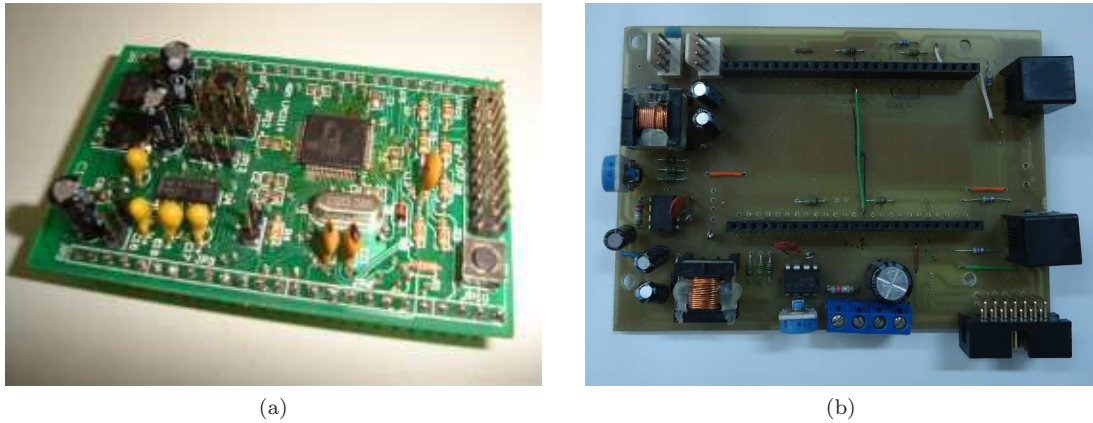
Versión preliminar de placas de circuito impreso (PCB) del controlador embebido utilizadas en el robot RoMAA. (a) PCB multipropósito del μC ARM7. (b) Soporte al PCB del μC , conectores y fuente.
